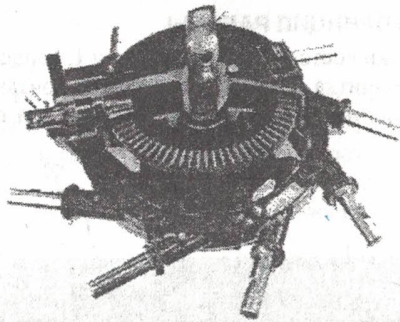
Принципиальное устройство корпуса зубчатой передачи с кареткой
